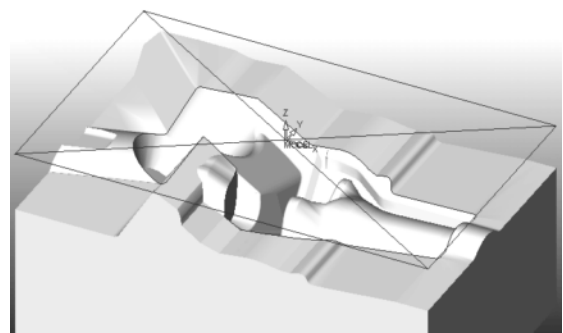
Загальний вигляд 3-D моделі частини штампу для виготовлення поковки лапи тришарашкового бурового долота
